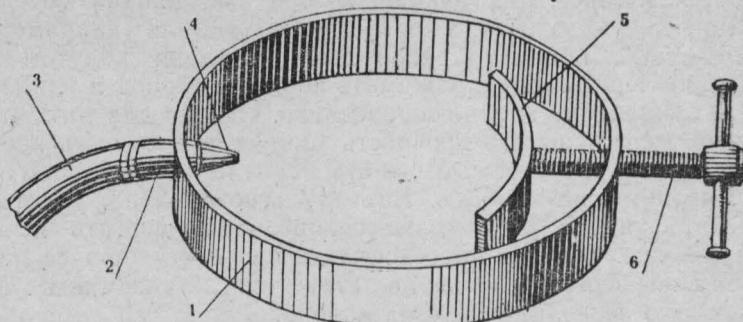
Приспособление для гидравлических испытаний корпусов огнетушителей через спрыск:
